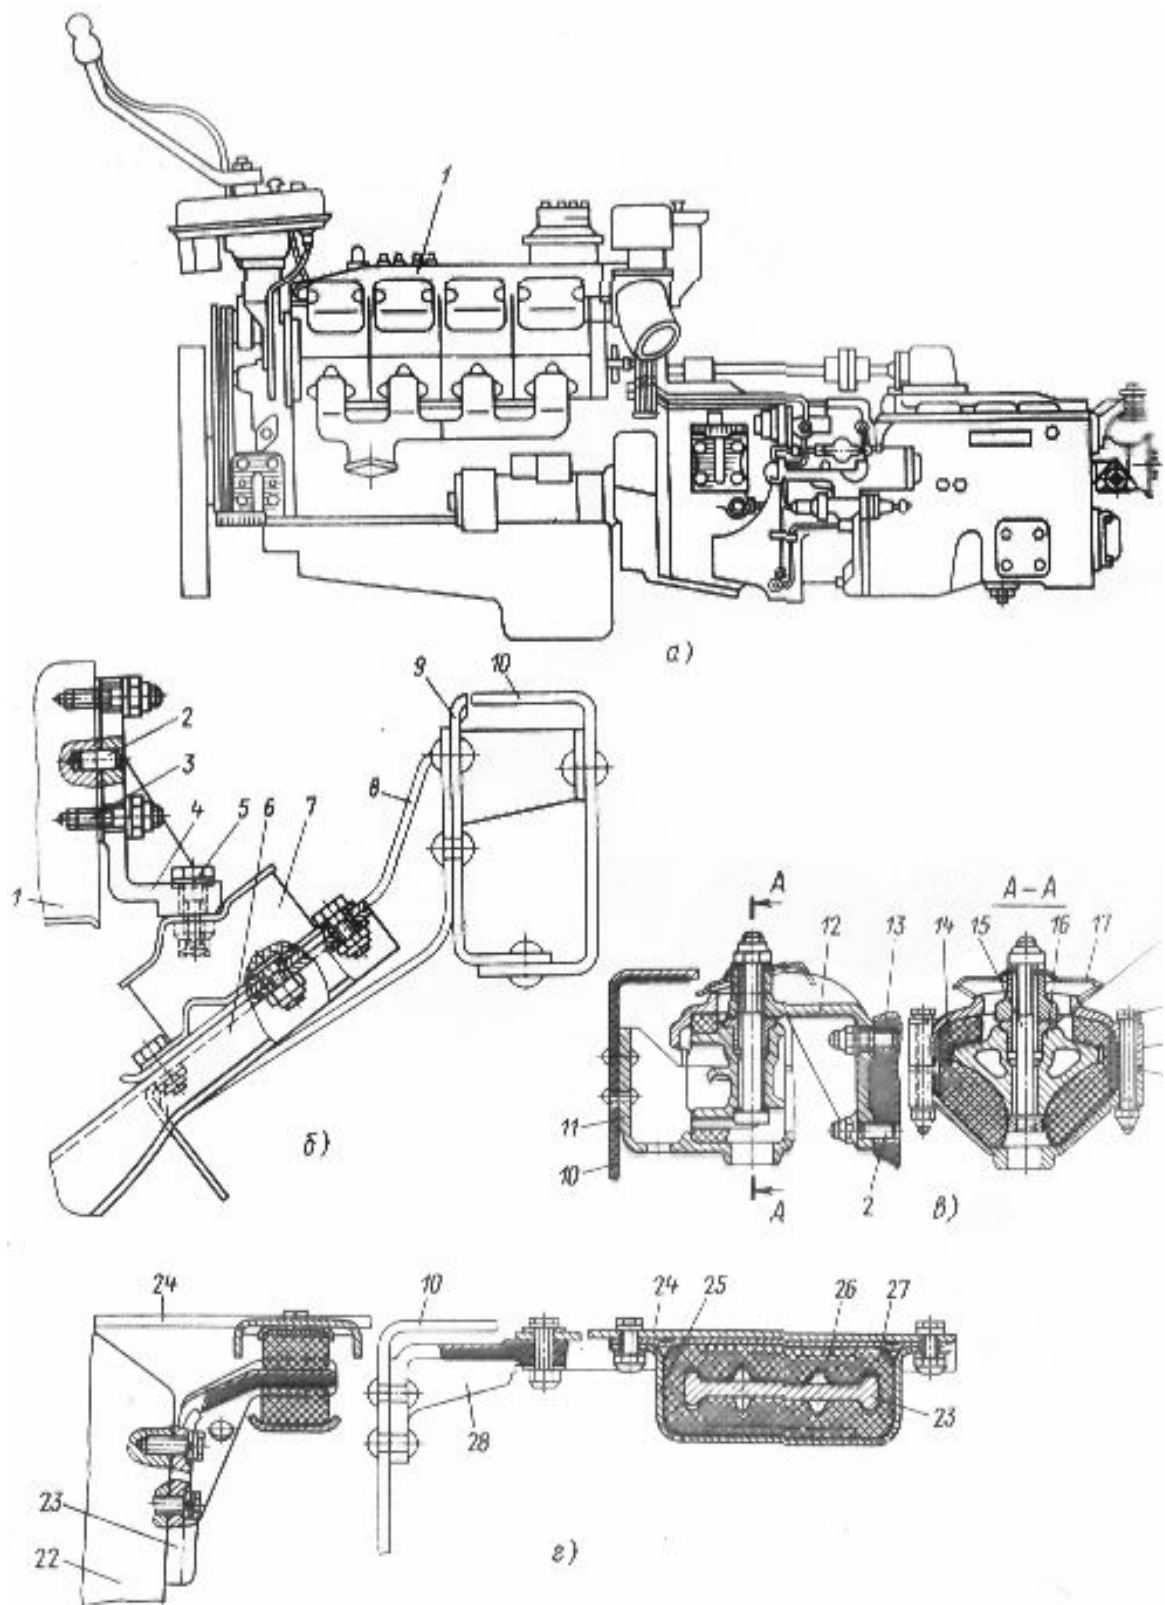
Силовой агрегат автомобиля КамАЗ-5320 и его крепление:
